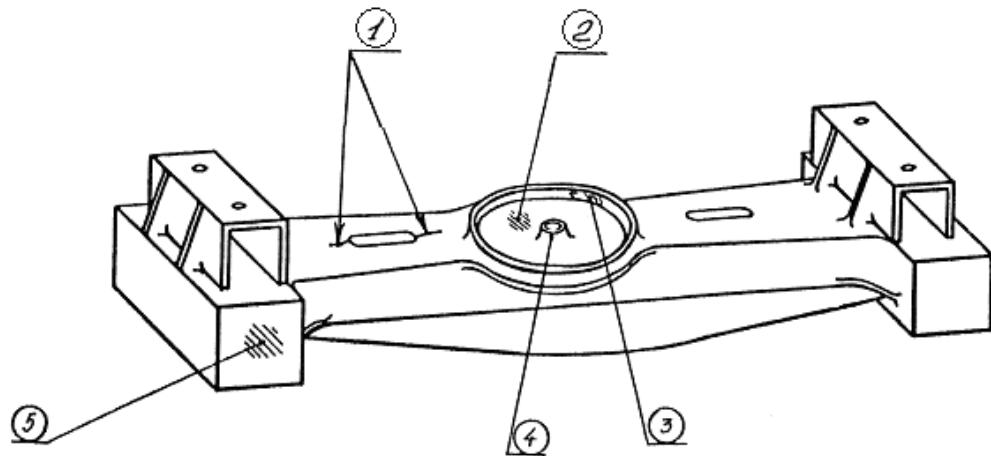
Основные дефекты литой балки надрессорной ЦМВ, ремонтируемые сваркой или наплавкой
